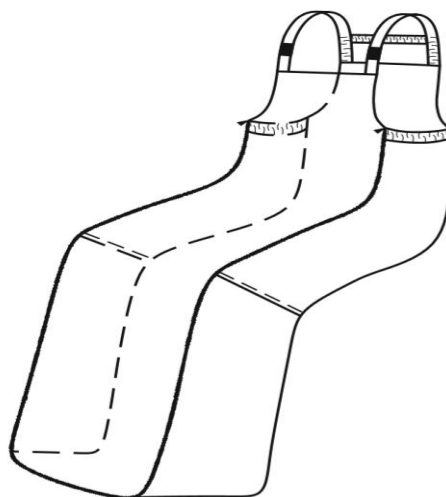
Внешний вид конструктивного устройства макета теплозащитного изделия
